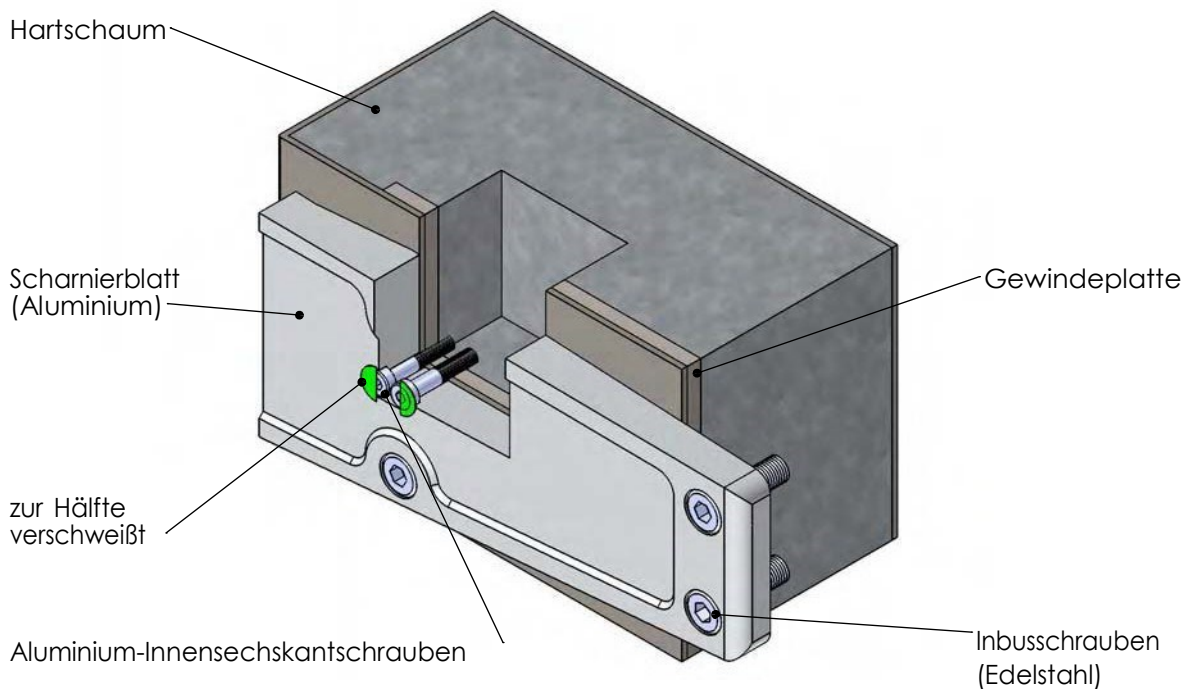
Sicherung mit Aluminiumlinsenschrauben
